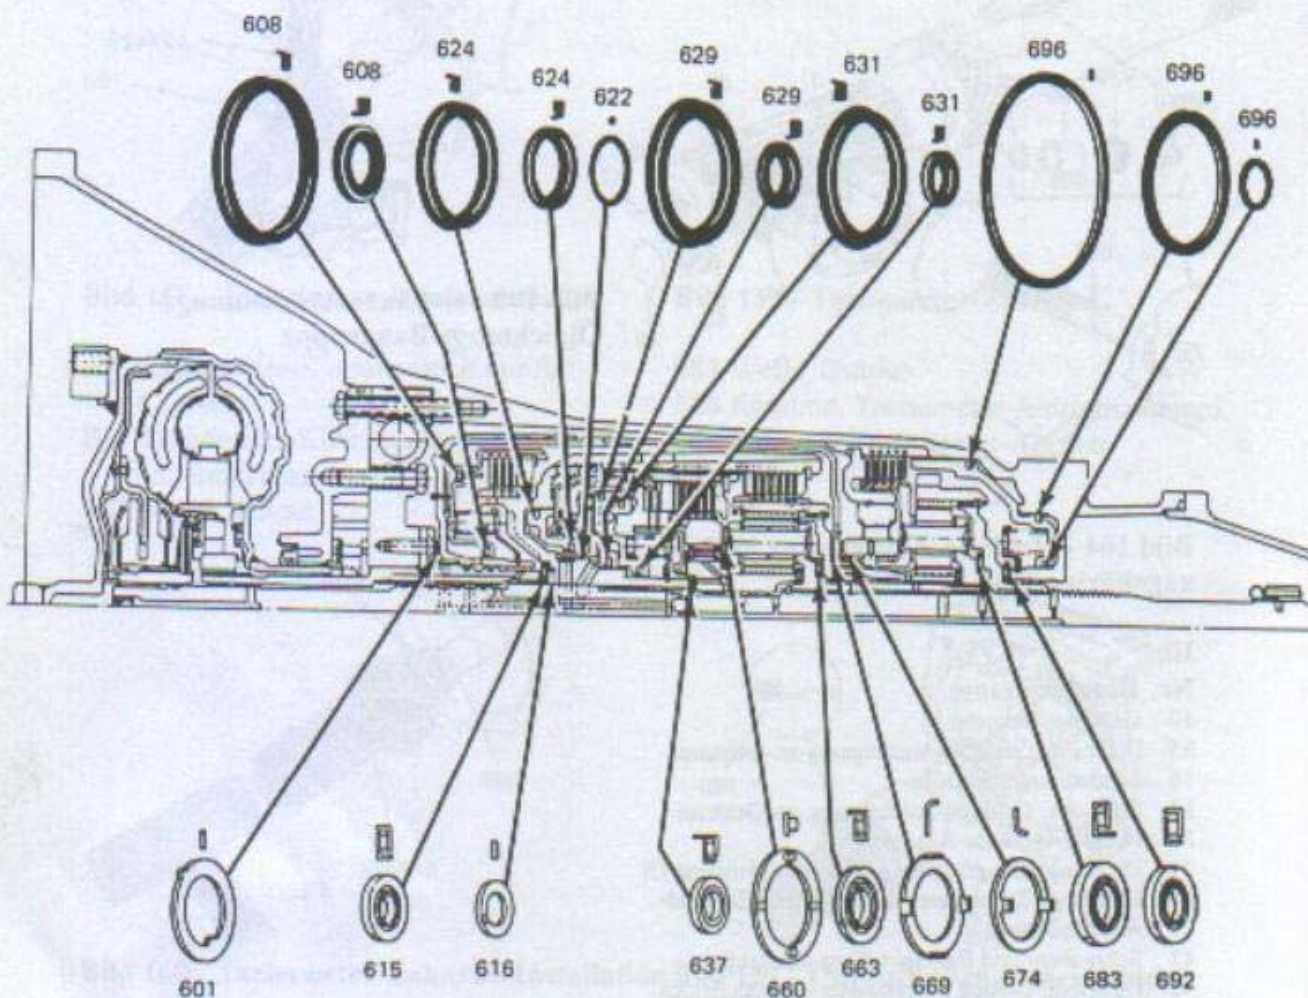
Gehäuse-Ausdehnungs-Öldichtungs-Baugruppe
